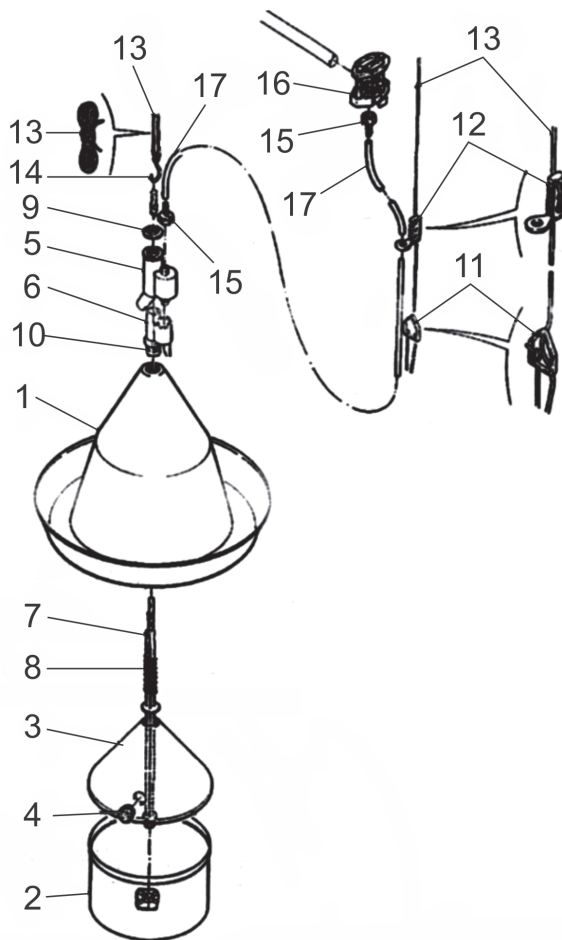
Круглая поилка: 1 – колокол поилки; 2 – нижняя часть поилки; 3 – крышка; 4 – заглушка; 5 – корпус клапана внешний; 6 – корпус клапана внутренний; 7 – подвесной стержень; 8 – пружина большая; 9 – контргайка; 10 – клапанное устройство; 11 – натяжное устройство для подвесного каната; 12 – направляющие шланги; 13 – подвесной канат; 14 – S-крюк; 15 – наконечник; 16 – заслонка; 17 – шланг
